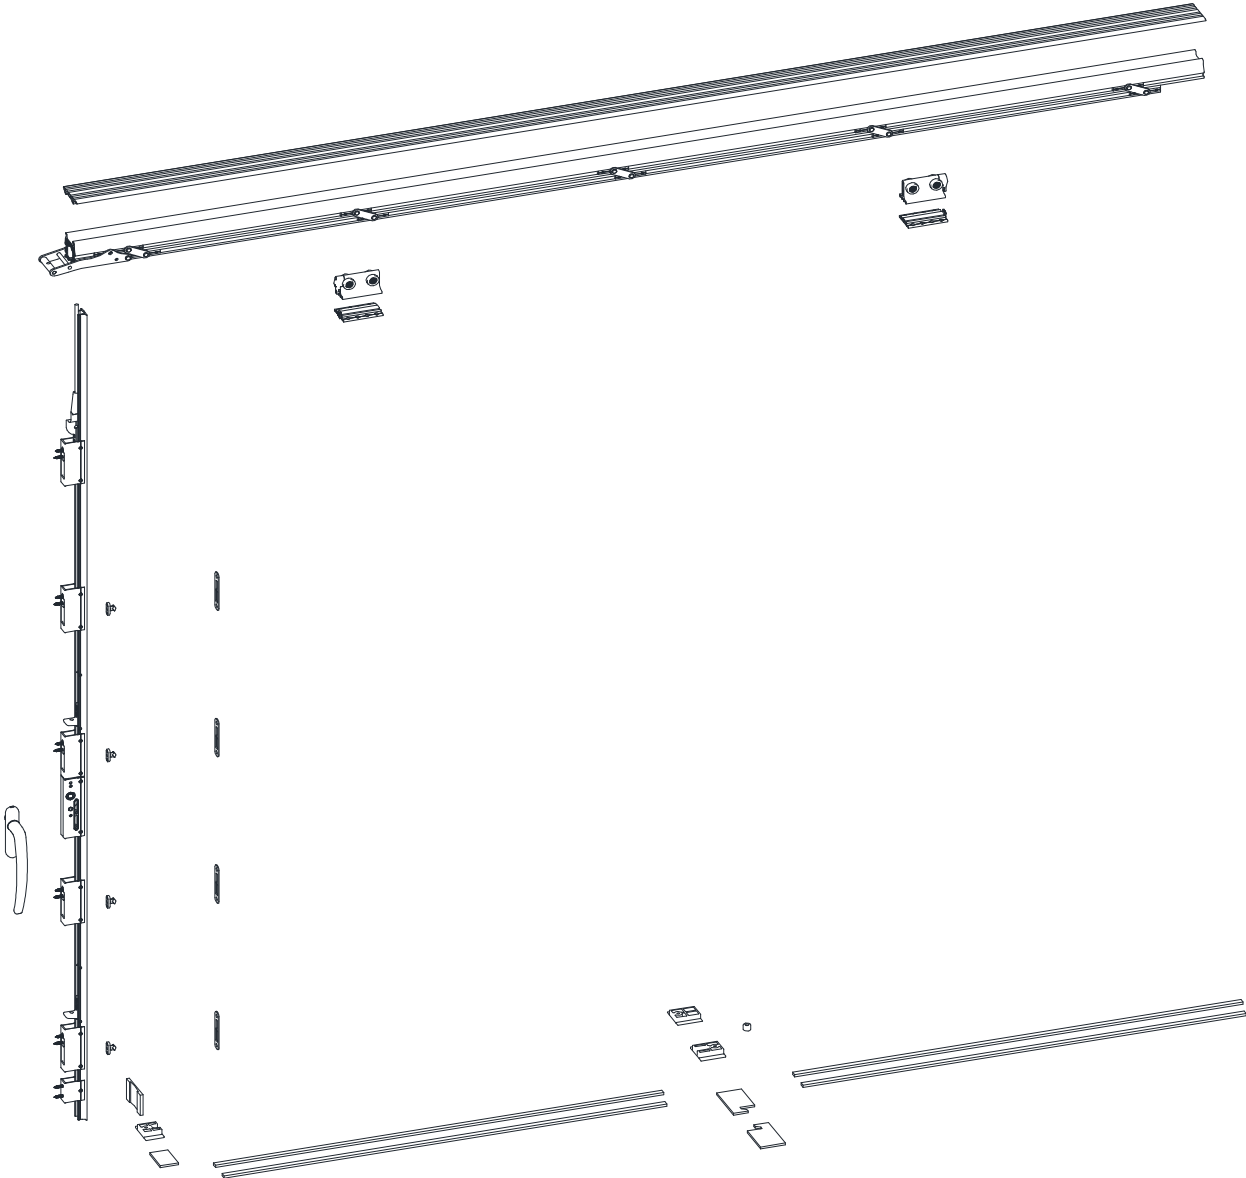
Détail des accessoires de la maquette soumise à l'essai
